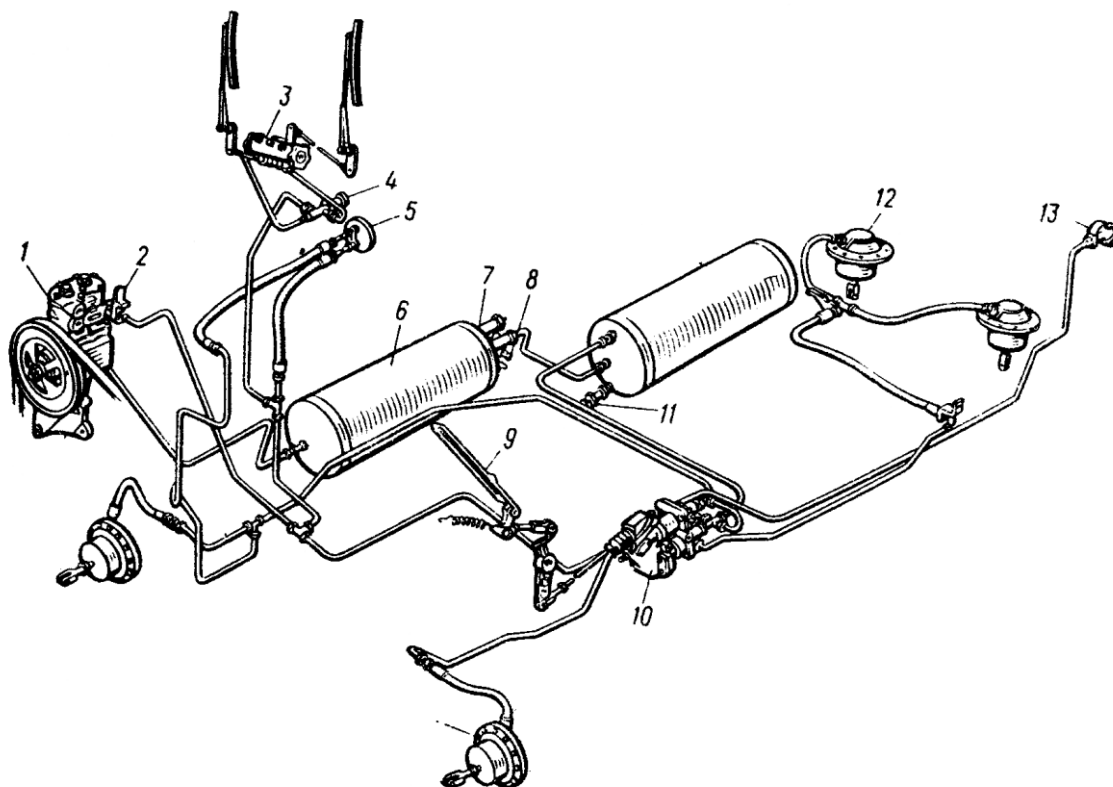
Пневматический тормозной привод автомобиля ЗИЛ-431410: 1 – компрессор, 2 – регулятор давления, 3 – механизм стеклоочистителя, 4 – головка управления стеклоочистителем, 5 – манометр, 6 – воздушный баллон, 7 – предохранительный клапан, 8 – кран отбора воздуха, 9 – педаль тормоза, 10 – тормозной кран, 11 – сливной кран, 12 – тормозная камера, 13 – разобцительный кран
